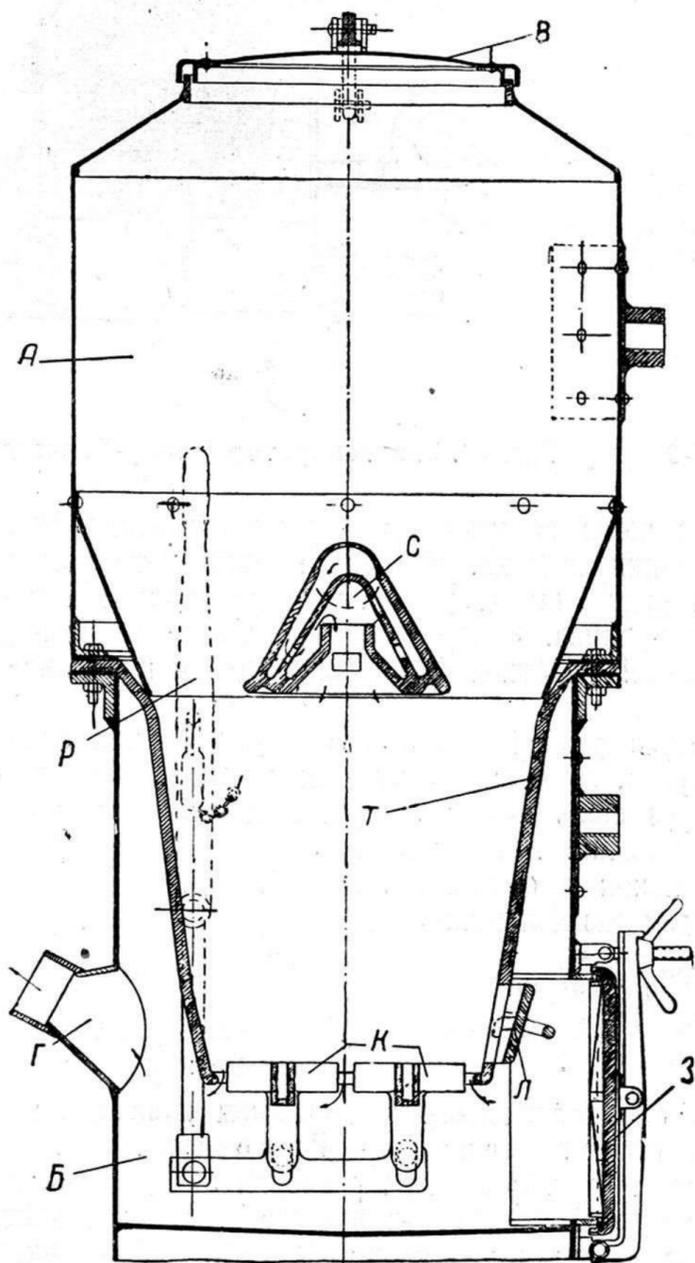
Газогенератор Рено для трактора Рено. А—бункер; Б—шахта; Т—топливник; К—качающиеся колосники; Р—ручка для встряхивания колосников; З—зольниковый люк; Л—люк для чистки топливника. В—загрузочный люк; Г—газоотсасывающий патрубок; С—воздушное сопло
